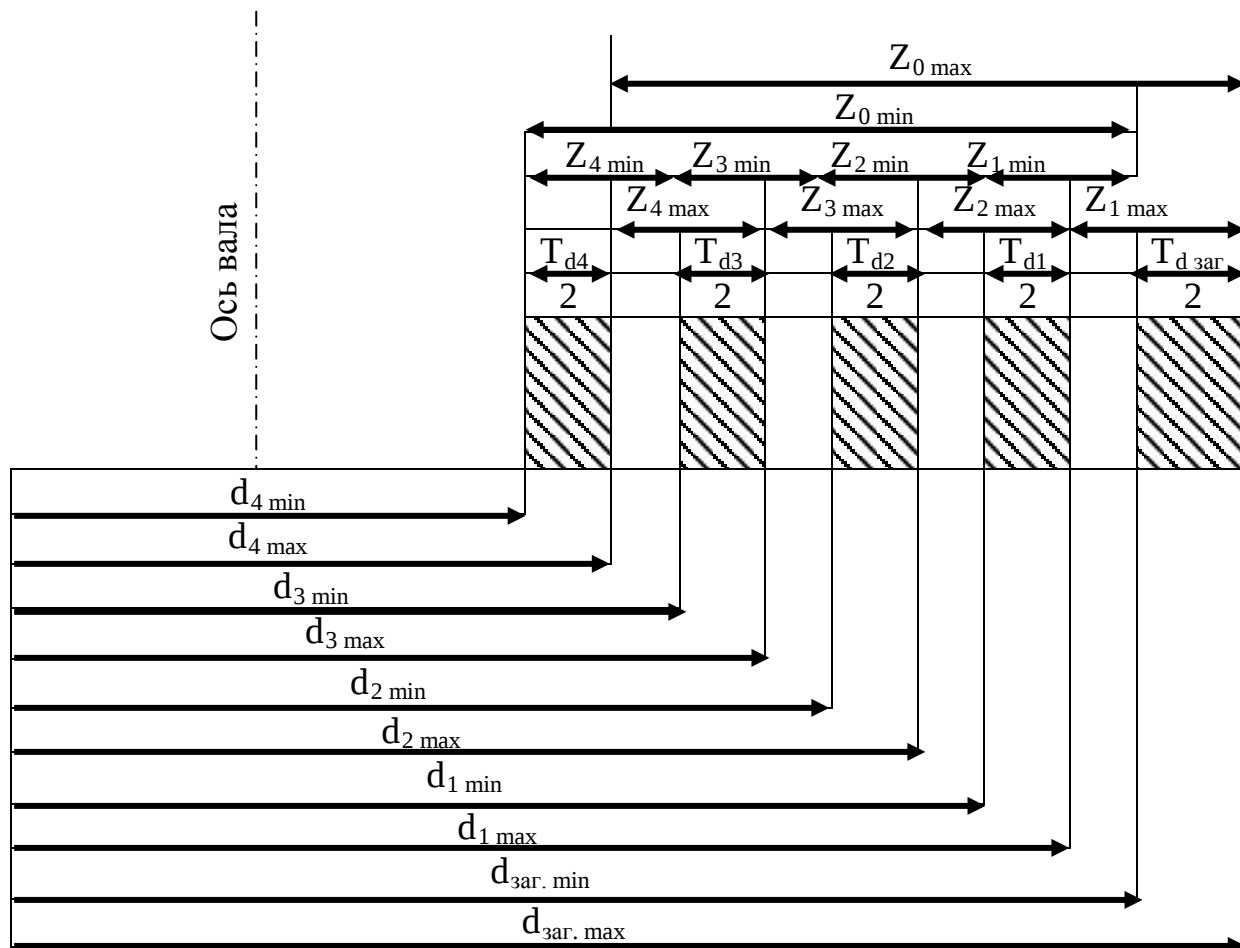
Схема расположения размеров, полей припусков и допусков при обработке вала:
